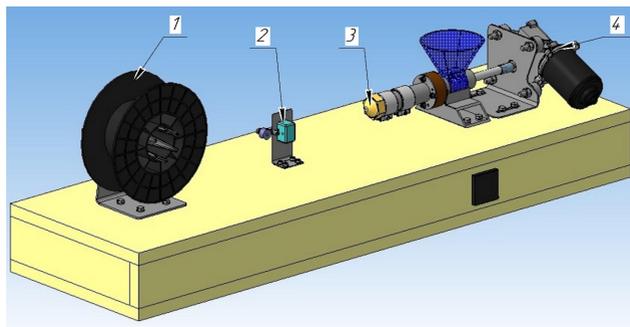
Филаментный экструдер: 1 – сматывающая катушка; 2 – устройство контроля диаметра; 3 – сопло; 4 – электромотор
